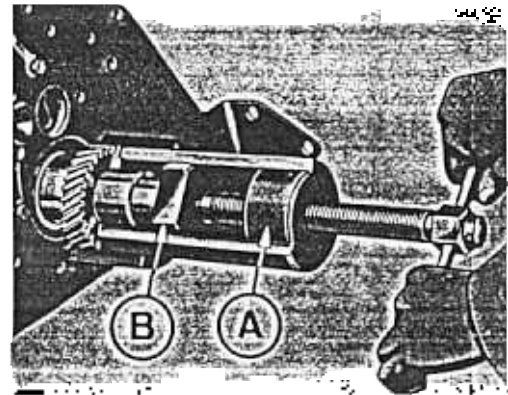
A-14E-02 Extracción del engranaje del cigüeñal
